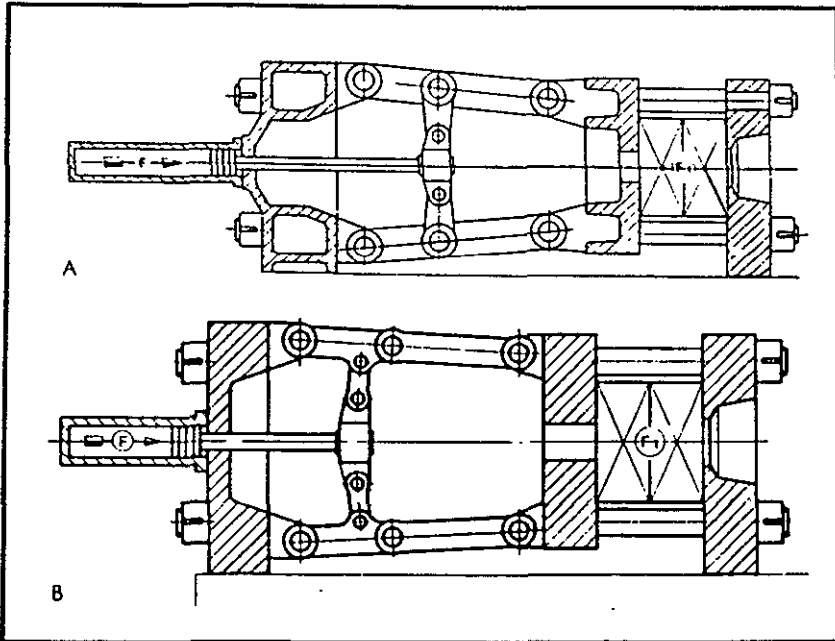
Cierre de Molde Tipo Doble Rodillera.
